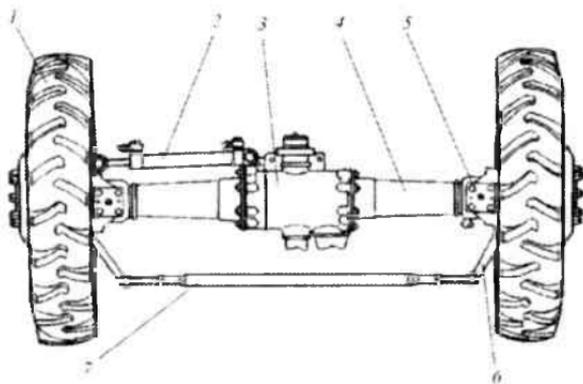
Передний ведущий мост трактора ТТЗ-82 М, вид. Сверху: 1 – колесо; 2 – гидроцилиндр; 3 – дифференциал; 4 – балка; 5 – цапфа; 6 – рычаг; 7 – тяга
